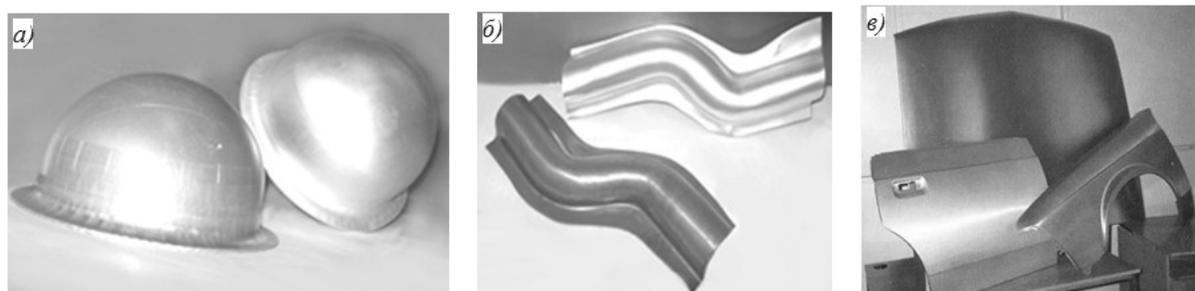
Детали из сплава В-1341, полученные холодной деформацией: а – днище бака; б – полупатрубок; в – панели кузова [32, 65]
